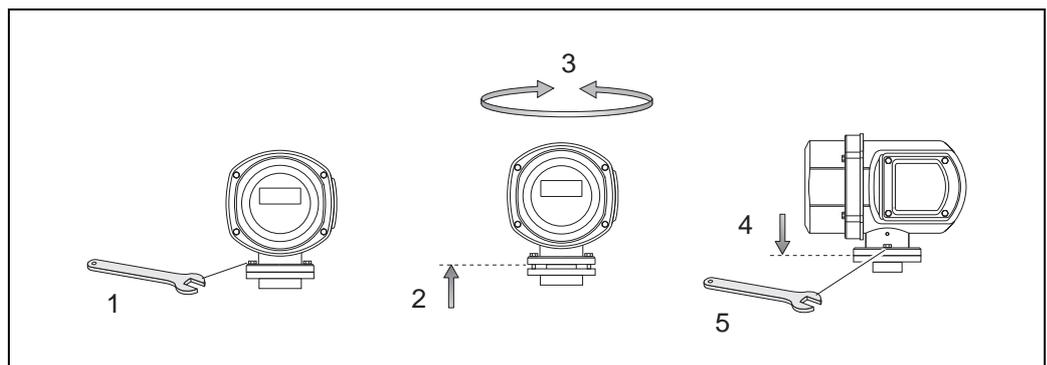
Drehen des Messumformergehäuses (Edelstahl-Feldgehäuse)
